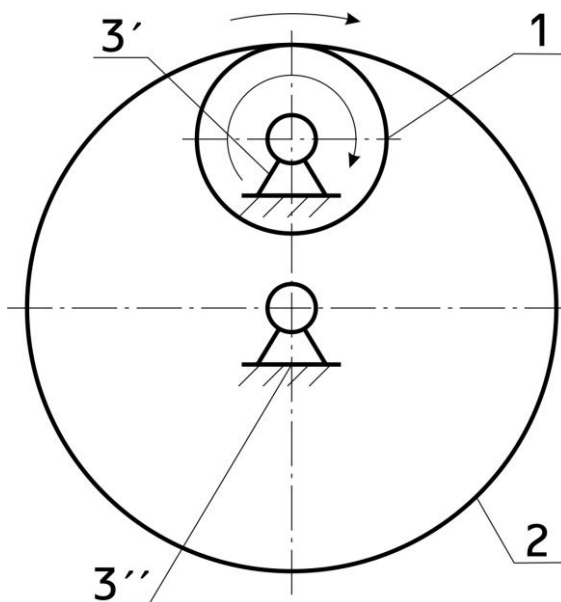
Зубчатый механизм с внутренним зацеплением
